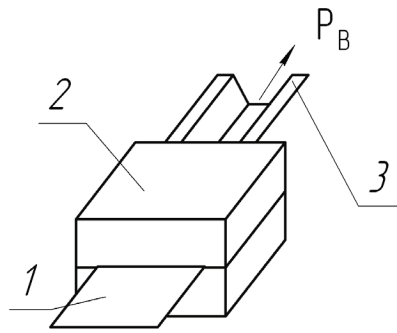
Формоутворення профілю під час протягування заготовки через інструментальну фільтру: 1 – листова заготовка; 2 – фільтр; 3 – профіль
